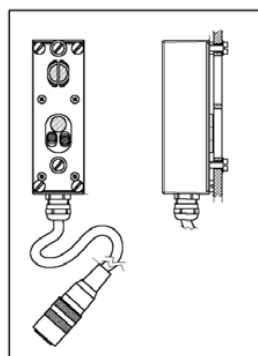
Sensore con cavo fisso. Fixed cable sensor.
